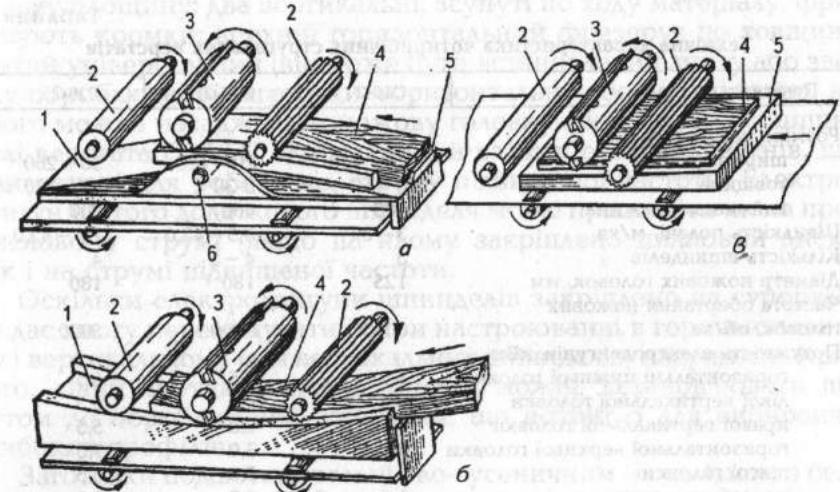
Пристрій для стругання заготовок на рейсмусових верстатах з поверхнею:
